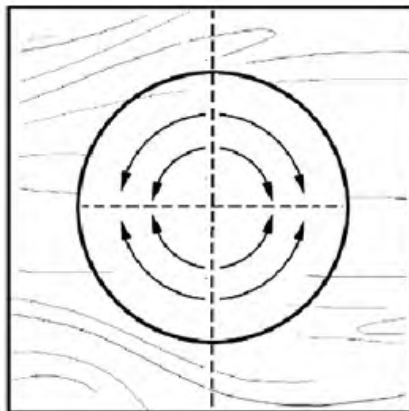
Выполнение круглой выпуклой формы на пласти заготовки (стрелками указано направление движения инструмента)
